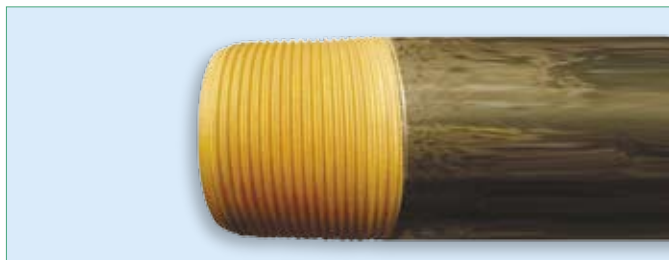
Внешний вид трубной резьбы с нанесенным покрытием
